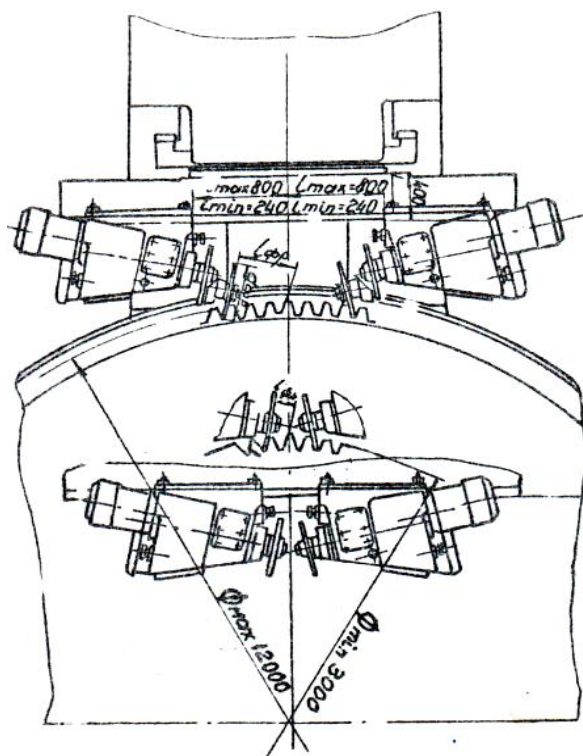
Схема двухшпиндельного суппорта к вертикально-зубофрезерным станкам мод. 5В345П, 5В348, 5В348/12,5, КУ-279
